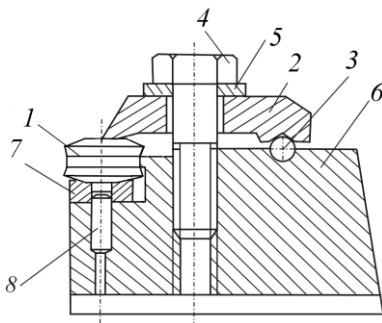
Узел крепления режущей пластины из ПКНБ с вертикальной и горизонтальной осями симметрии. 1 – режущая пластина; 2 – прихват; 3 – шарик; 4 – прижимной болт; 5 – шайба; 6 – корпус державки; 7 – сепаратор; 8 – штифт
